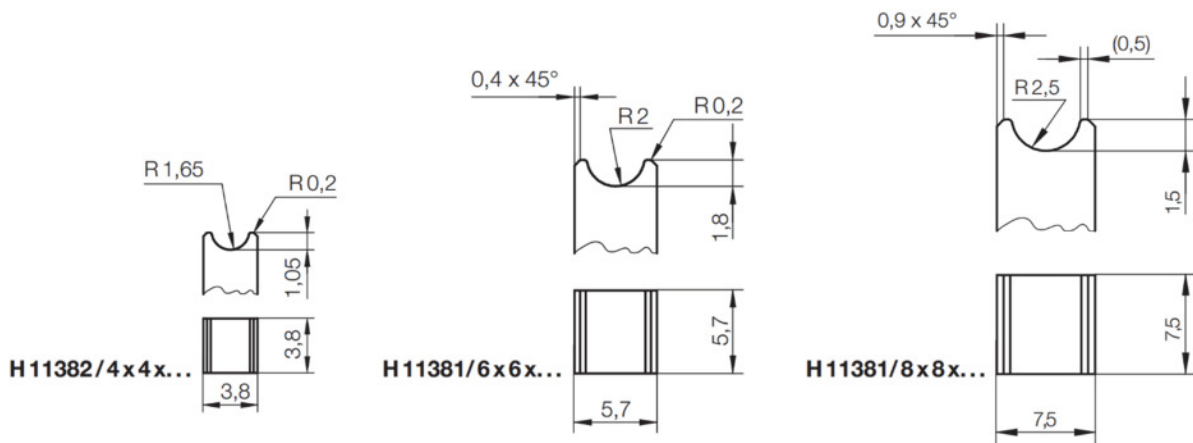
Инструмент для укладки трубчатого нагревателя
